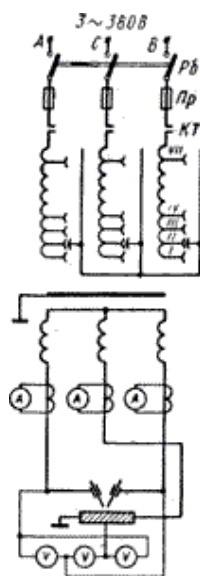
Принципиальная электрическая схема трансформатора ТСП-180 для сварки трехфазной дугой
